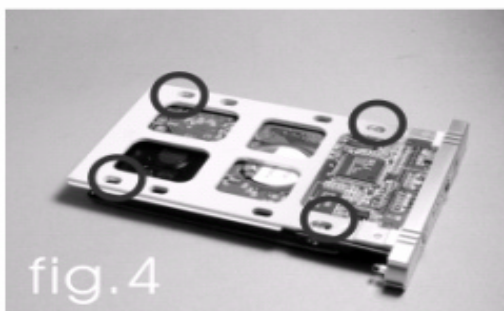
Schrauben Sie die Festplatte mit vier Schrauben fest auf den Schlitten.
